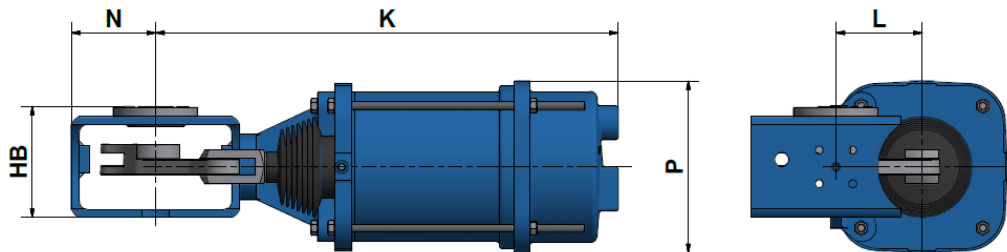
Maßzeichnung für Antriebe Typ R mit Konsole
